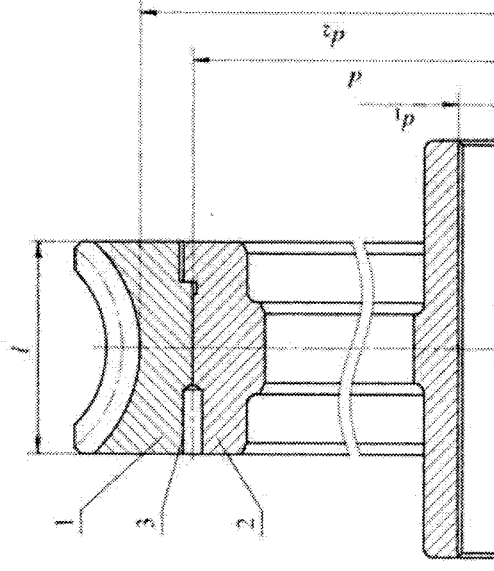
Соединение зубчатого венца со ступицей червячного колеса:
